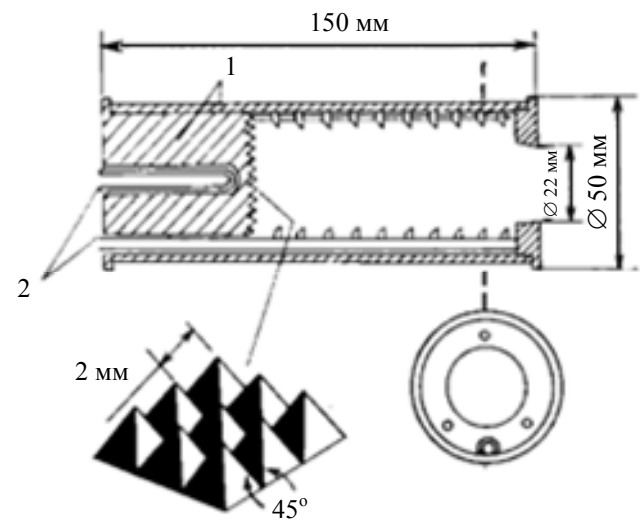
Конструкция цилиндрического черного тела с микропризматической торцевой поверхностью и отражательными перегородками по [15].
